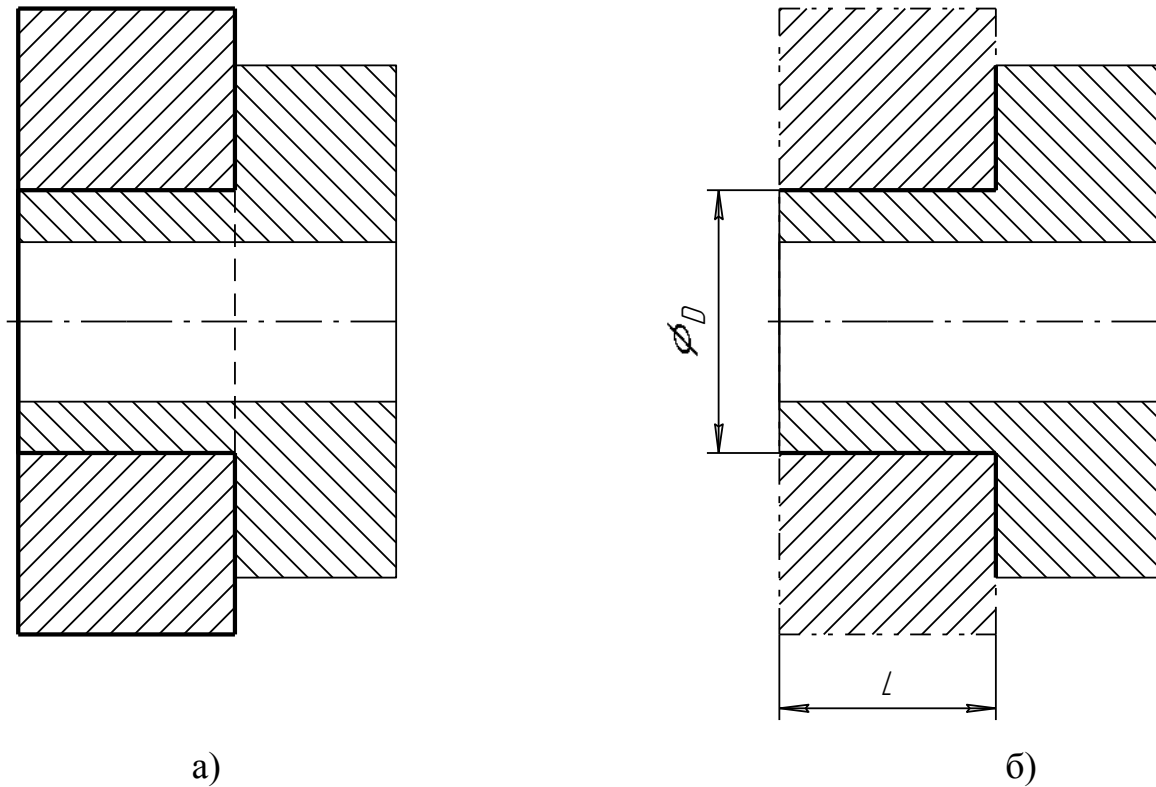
Пример оформления чертежа удаляемой части чертежа
